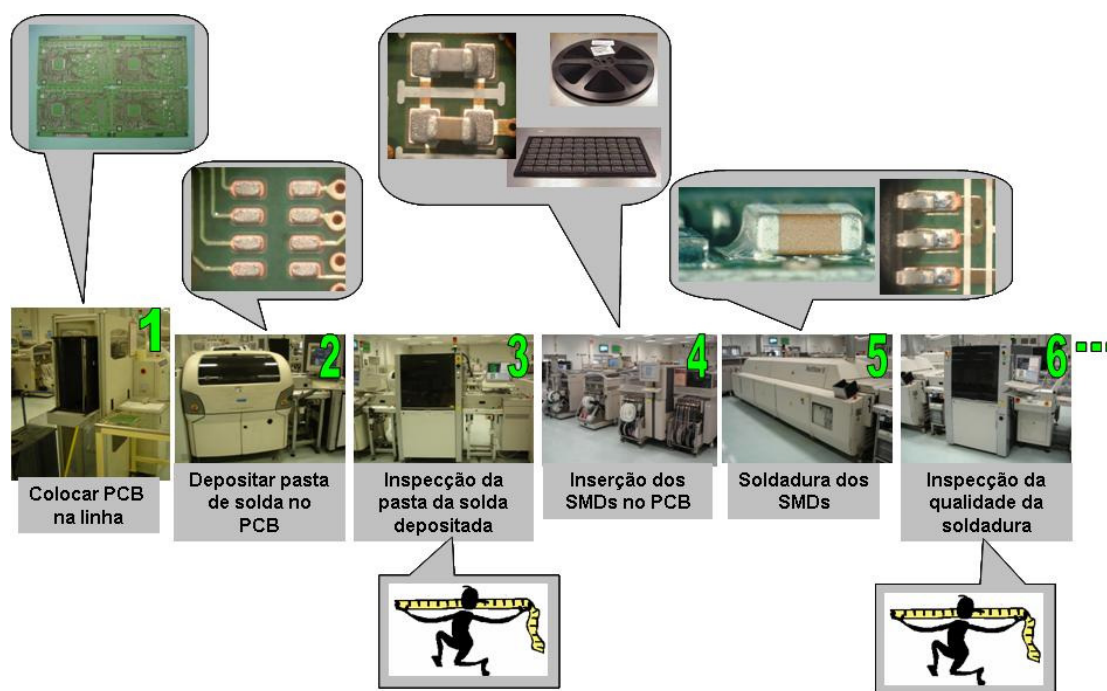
Diagrama de blocos do processo de soldadura *reflow
